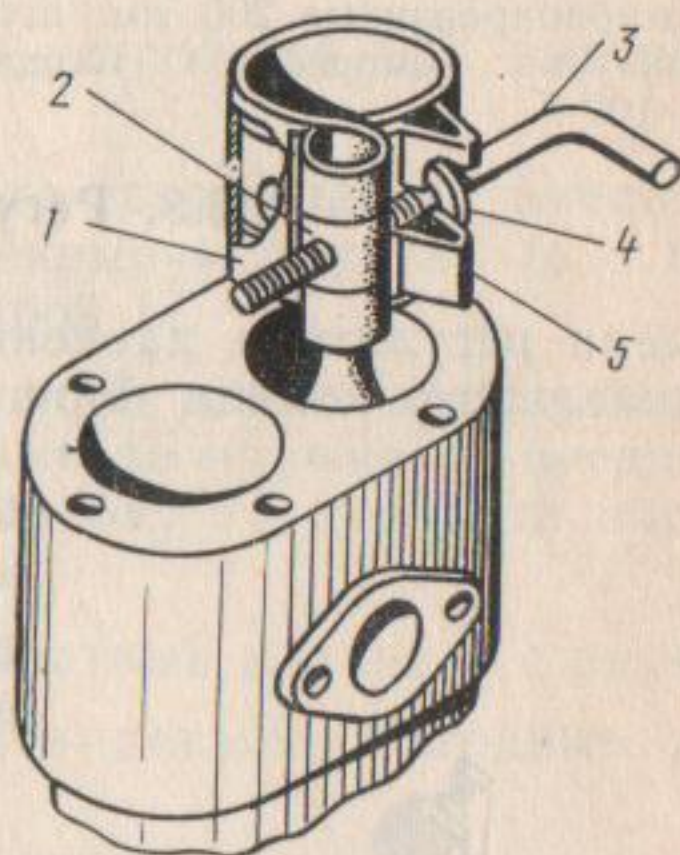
Установка поршня в сборе с шатуном и кольцами в цилиндр блока компрессора приспособлением 2494:
